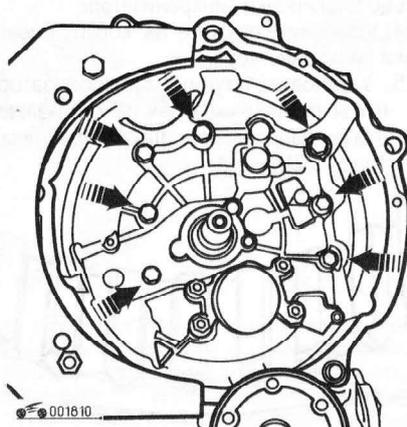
Расположение болтов крепления картера сцепления к картеру коробки передач
